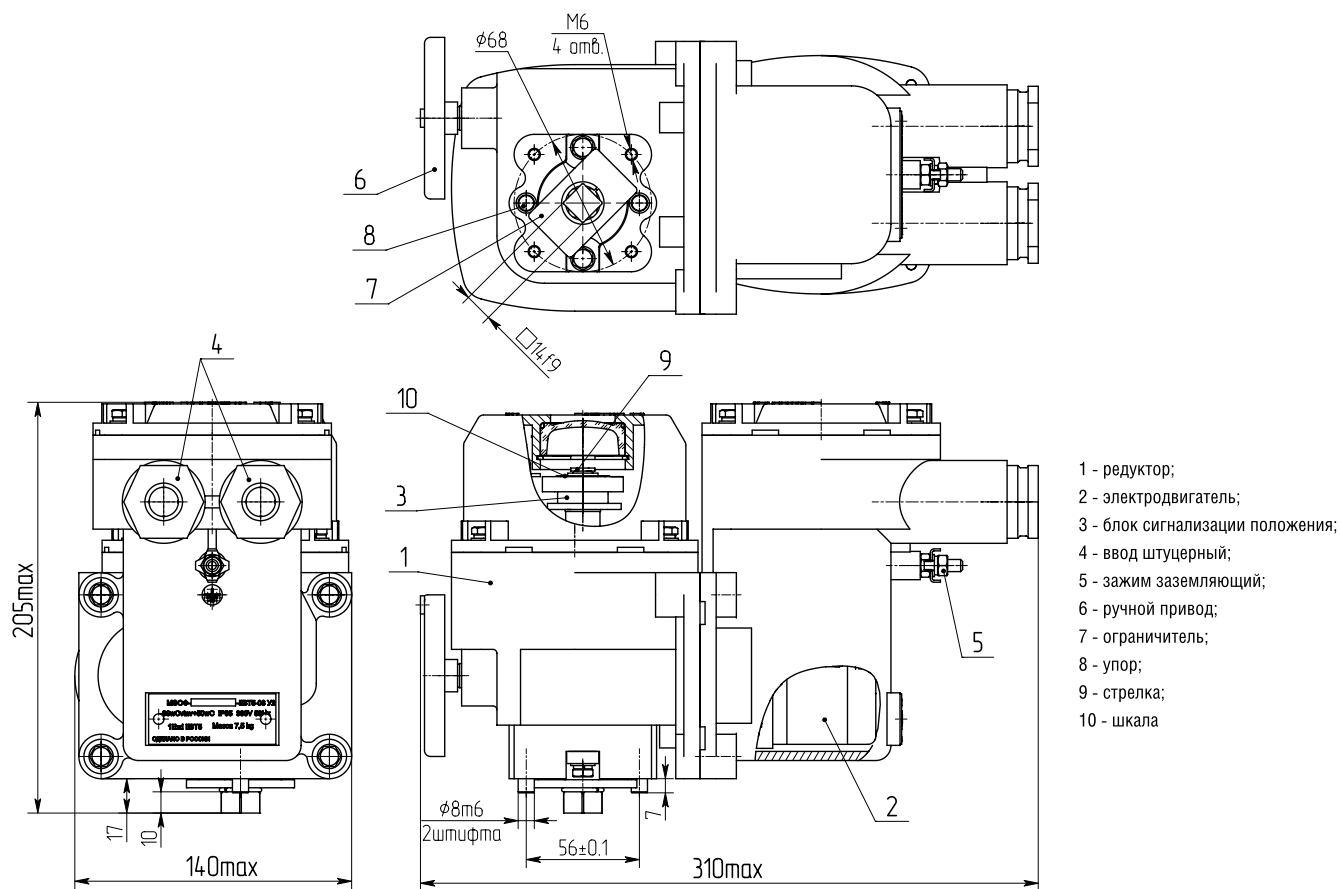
Габаритные и присоединительные размеры М30Ф-6,3-IBT5
